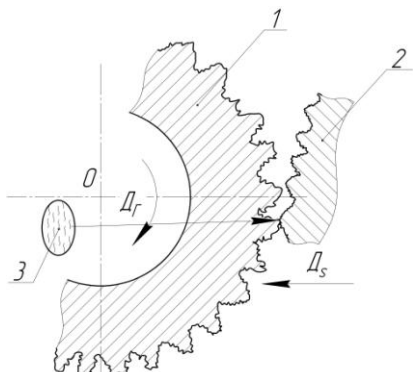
Схема концентрации напряжений, возникающей при силовом скольжении воздействию неровностей режущей кромки на неровности заготовки при точении: 1 – заготовка; 2 – режущая кромка; 3 – микротрещины фреттинга
